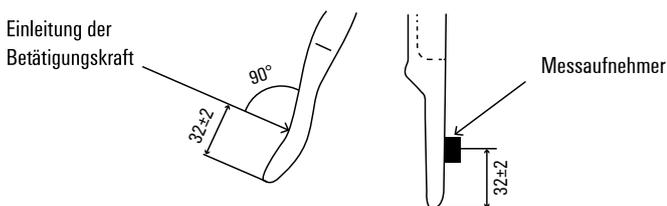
Anordnung des Werkzeuges in der Prüfeinrichtung des Werkzeugprüfstandes
